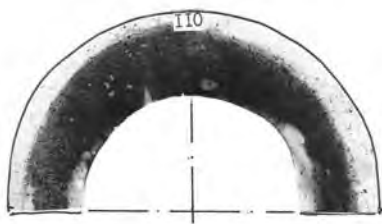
Серный отпечаток поперечного сечения отливки
